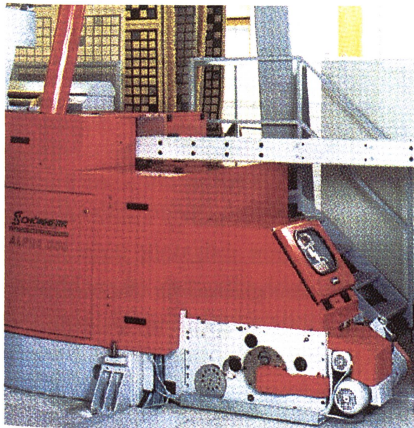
Elektronisch gesteuerte Rotations-Schaftmaschine 2685 an der Alpha 300
